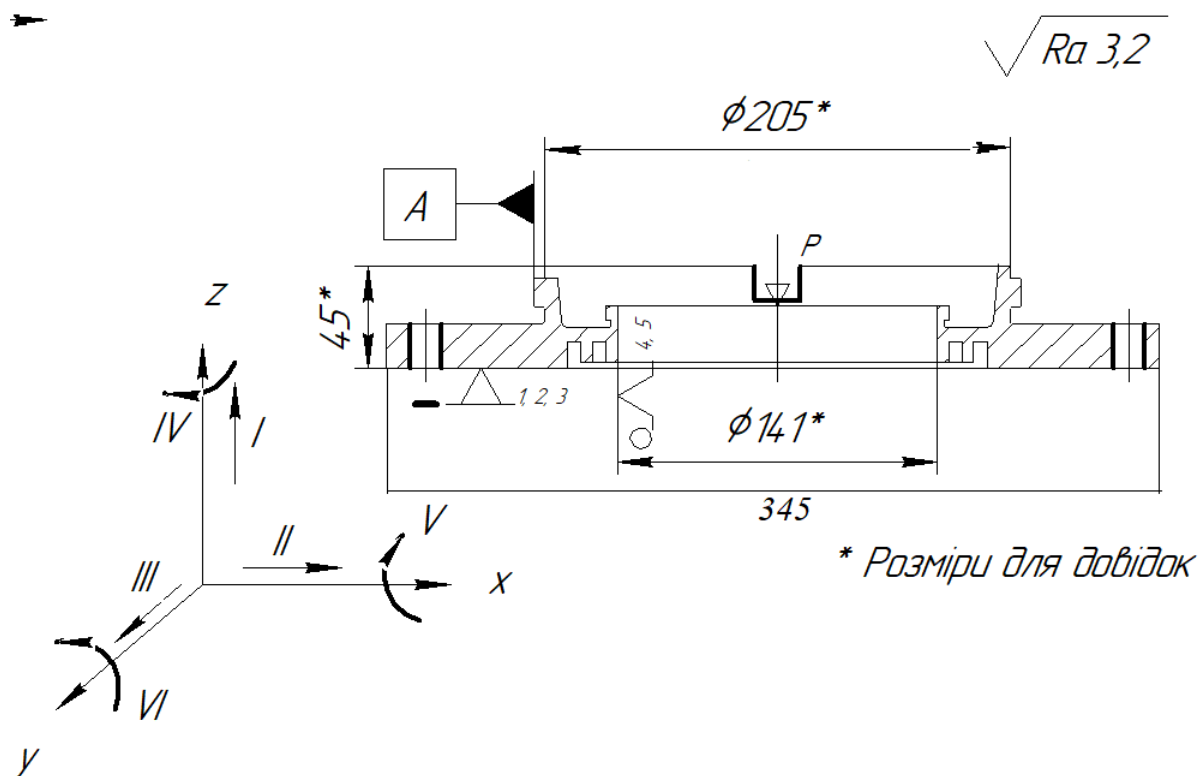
Схема базування деталі Кришка у вузлі
